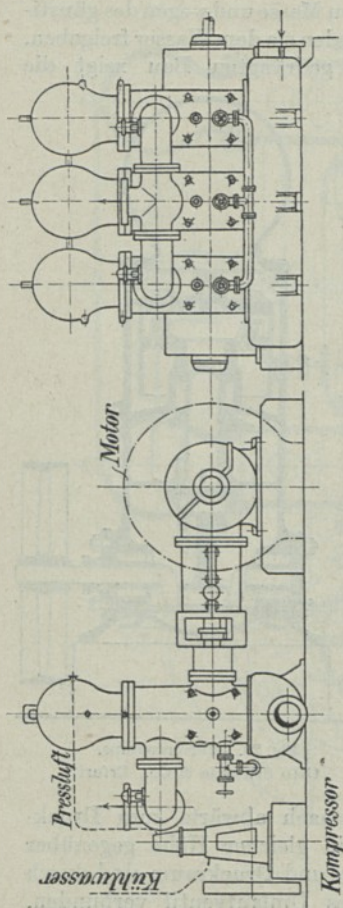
Drillingspumpe. Ehrhardt & Schmer, Schleifmühle-Saarbrücken.
